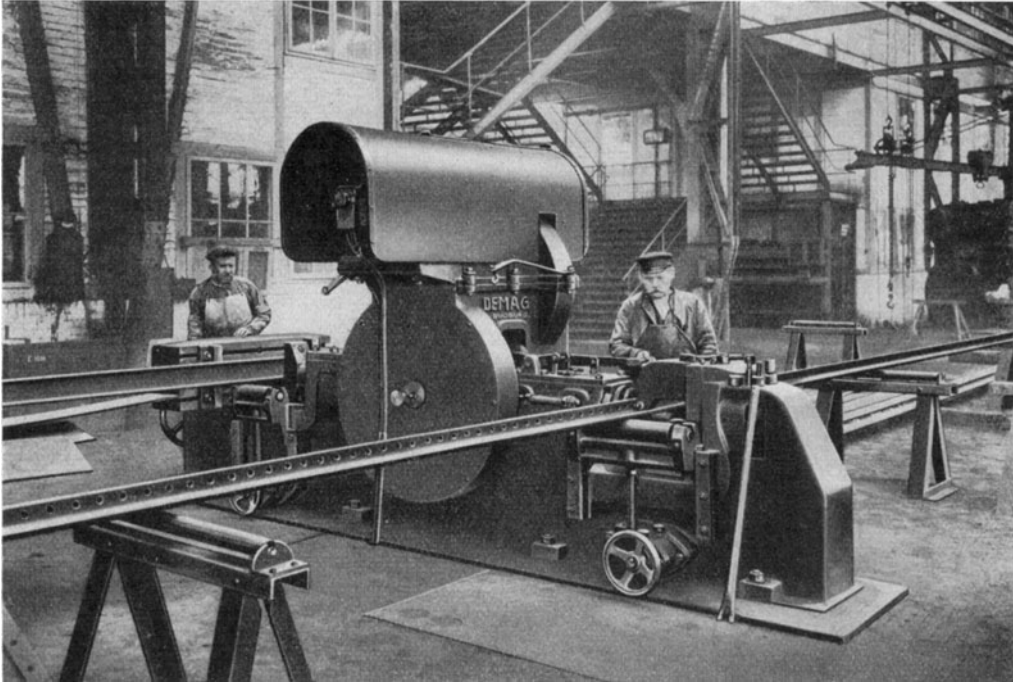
Horizontale Balkenbiege- und -lochmaschine.
